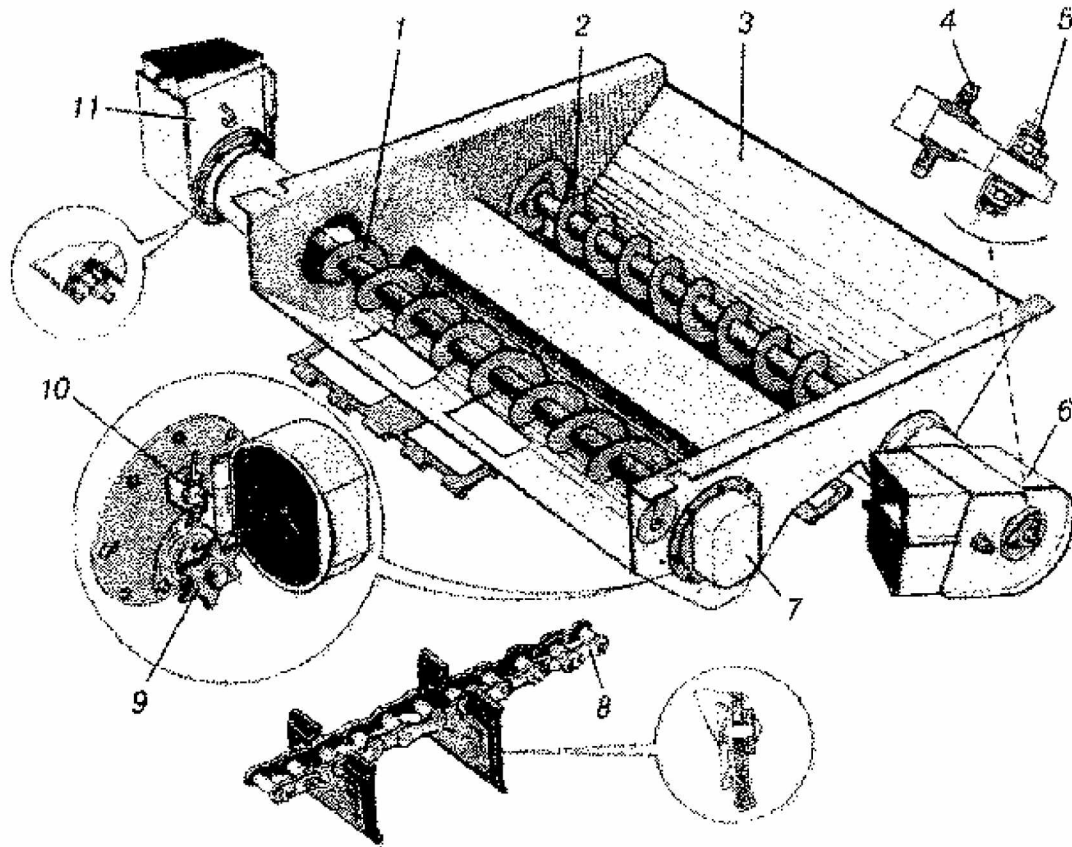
Нижній блок зернового та колосового шнека повітряно-решетної очистки зернозбирального комбайна КЗС-9-1 «Славутич»: 1 — шнек зерновий; 2 — шнек колосовий; 3 — корпус; 4,9 — зірочки трансмісії; 5 — підшипниковий вузол; 6 — скребковий елеватор колосовий; 7 — кожух; 8 — ланцюг; 10 — датчик; 11 — скребковий елеватор зерновий.
